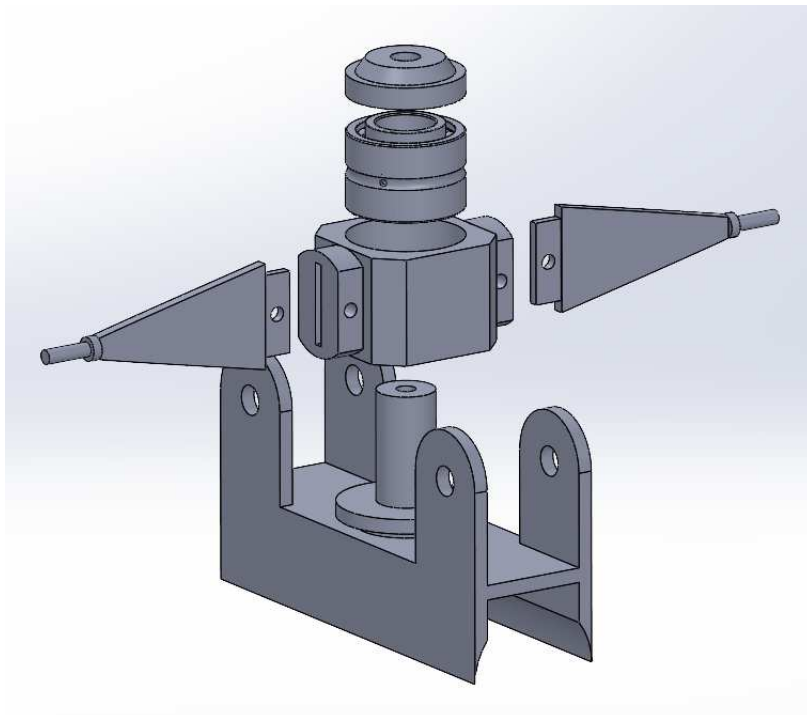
Vista explosionada del diseño de la barra estabilizadora de rigidez regulable mediante cambio de placas
